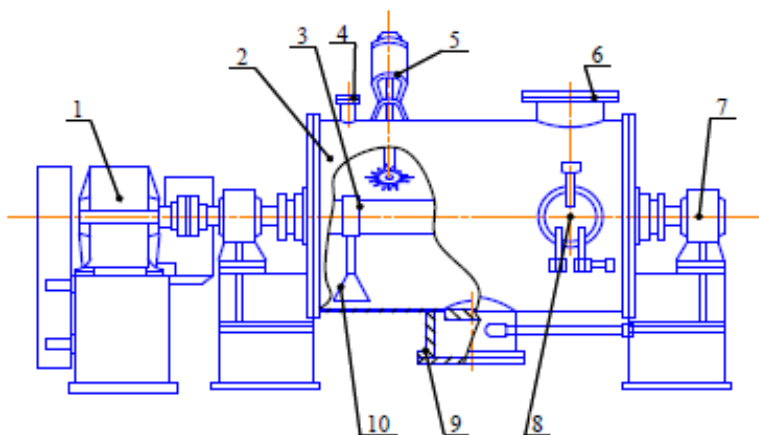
Плужковий змішувач типу СПЖ-500: 1 – електродвигун; 2 – корпус змішувача; 3 – вал; 4 – штуцер; 5 – електродвигун; 6 – завантажувальний патрубок; 7 – корпус підшипника; 8 – люк; 9 – вивантажувальний патрубок; 10 – лопаті [1].
